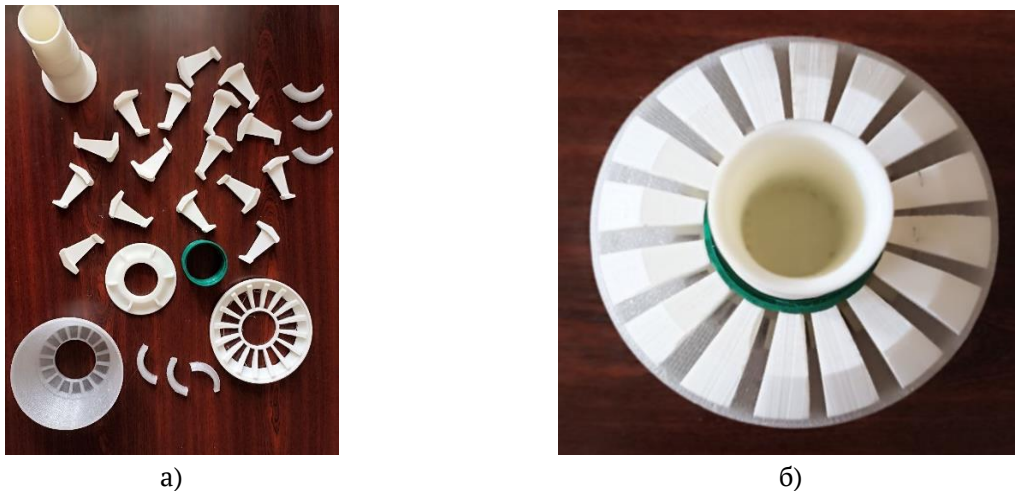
Виготовлені на 3D-принтері елементи конструкції пресформи та деталі ущільнювача превентора
